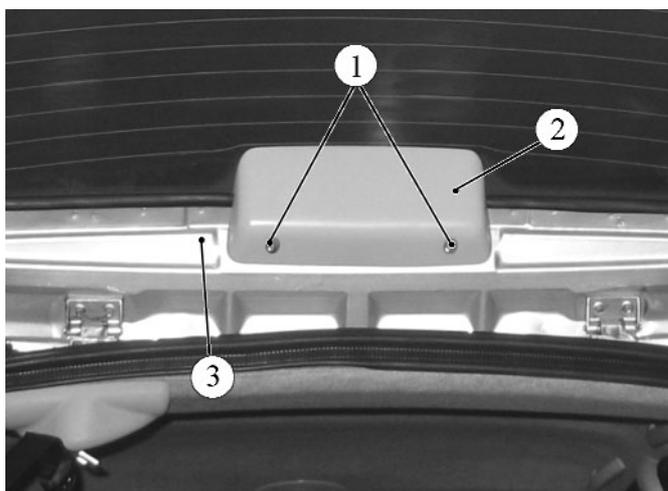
Крепление дополнительного сигнала торможения:
